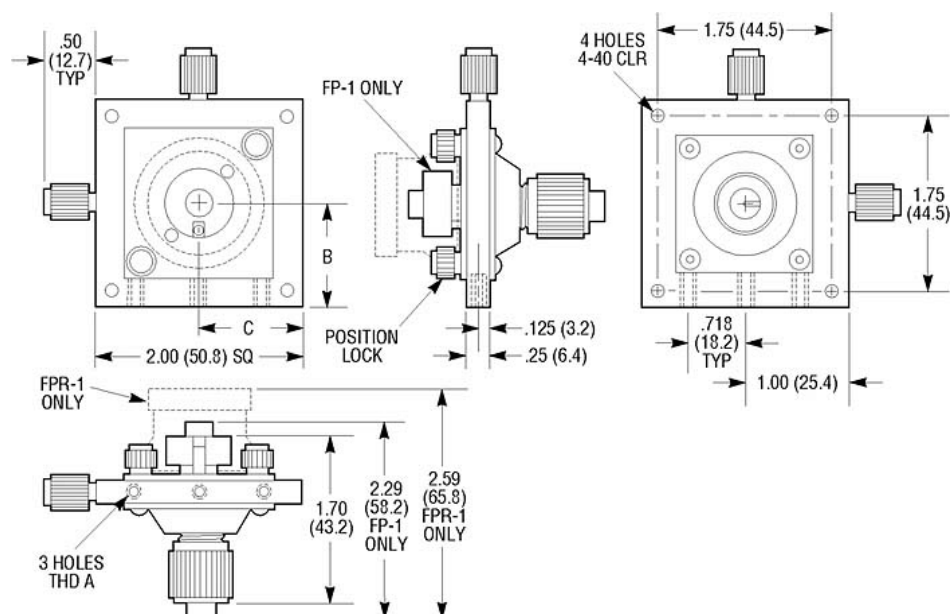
Representación esquemática del posicionador de fibra FP-1.
